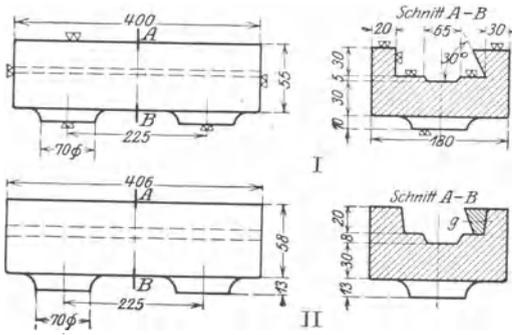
Schlittenführung. I. Werkstattzeichnung. II. Modellaufriß.
